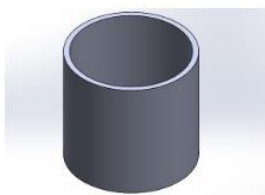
Cilindro oco que envolve as placas de circuito impresso. Fonte: Autoria própria.
